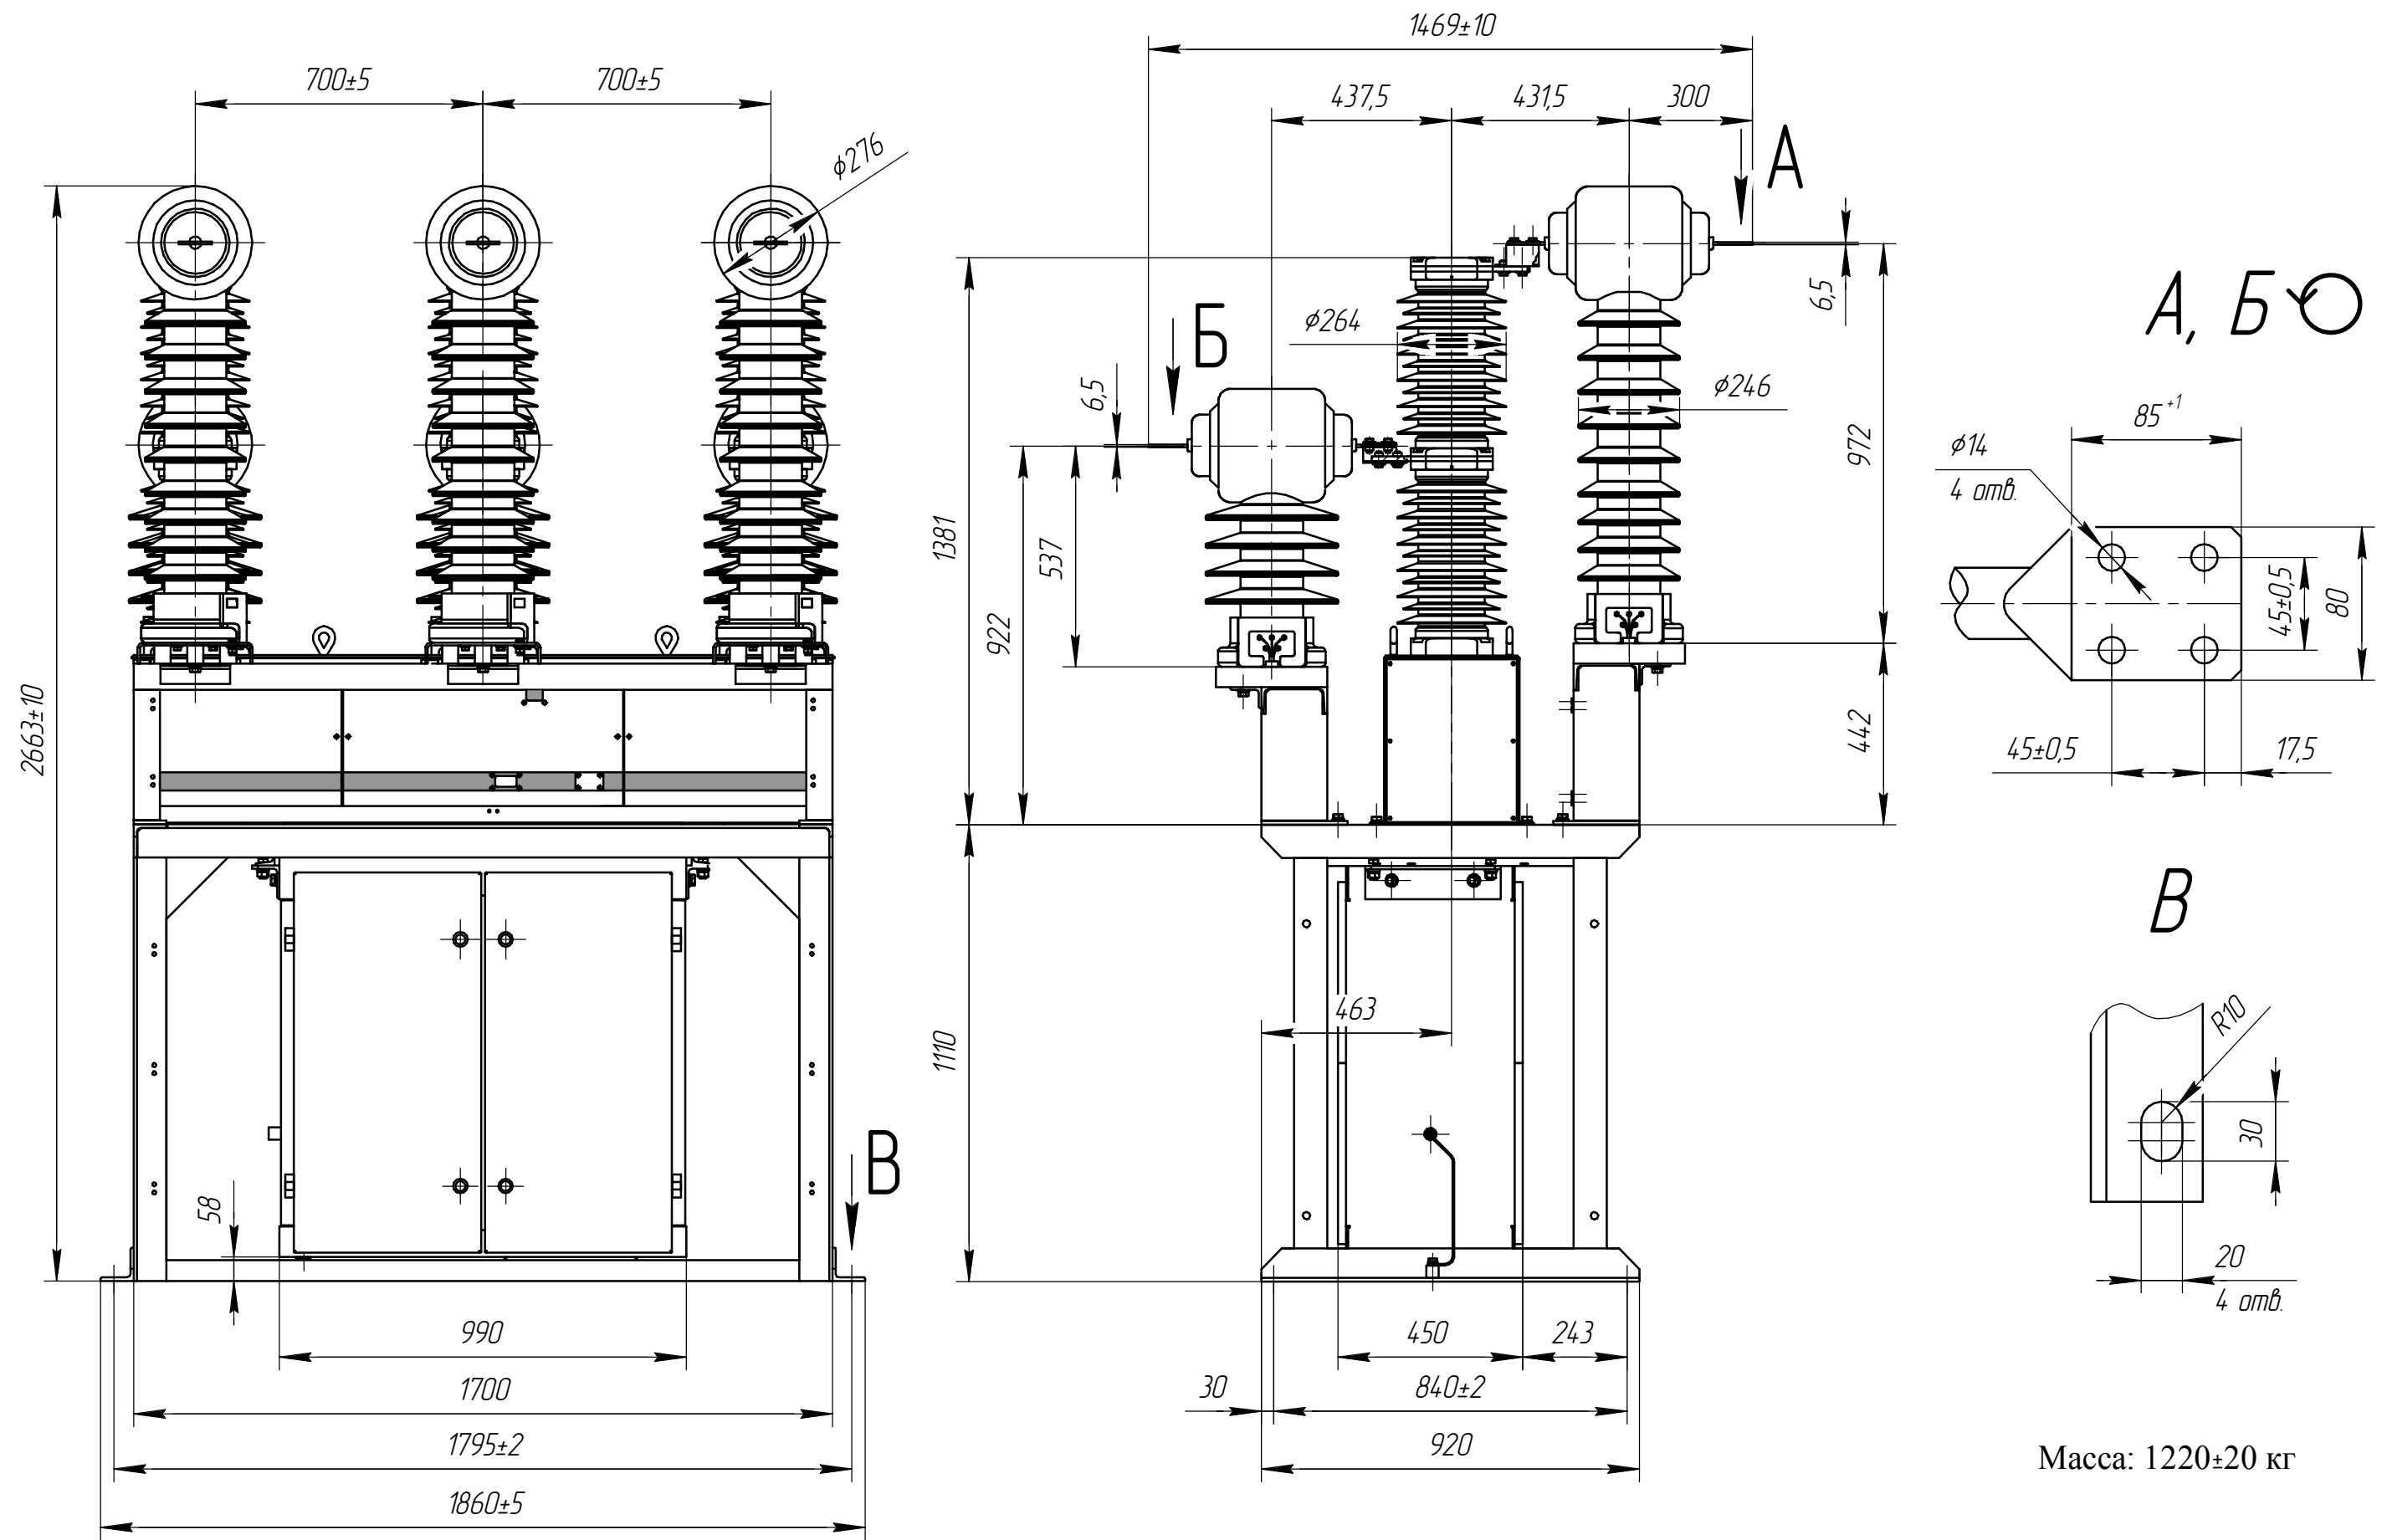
Габаритные, установочные и присоединительные размеры выключателя типоразмера ВР35НТ-35-25/1600-3/0 УХЛ1 с тремя встроенными трансформаторами тока ТОЛ-35 III-IV-1; 3; 5; 7 УХЛ1 со стороны нижних и ТОЛ-35 III-IV-2; 4; 6; 8 УХЛ1 со стороны верхних контактов
